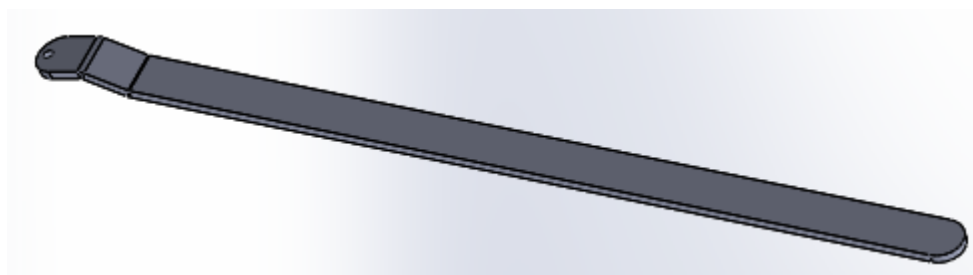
Palanca de la máquina de arrastre M-10 de BMM.
